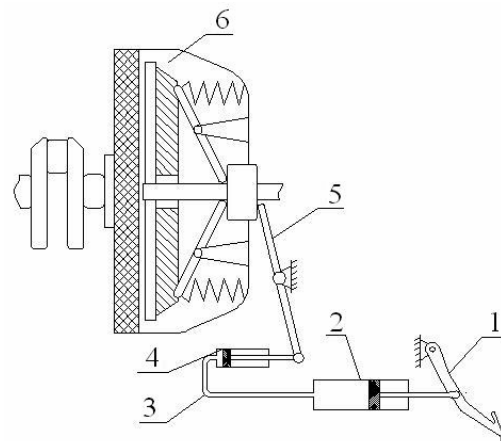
Схема гидравлического привода сцепления: 1 – педаль; 2 – главный цилиндр сцепления; 3 – трубопровод; 4 – рабочий цилиндр сцепления; 5 – вилка выключения сцепления; 6 – сцепление
